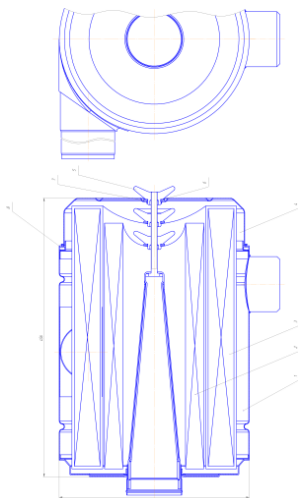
Предлагаемая конструкция воздухоочистителя
